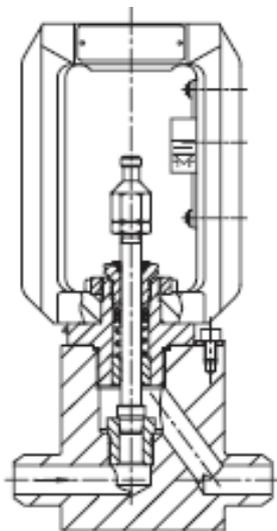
· Клапан высокого давления тип 3252 проходной с приварными концами
